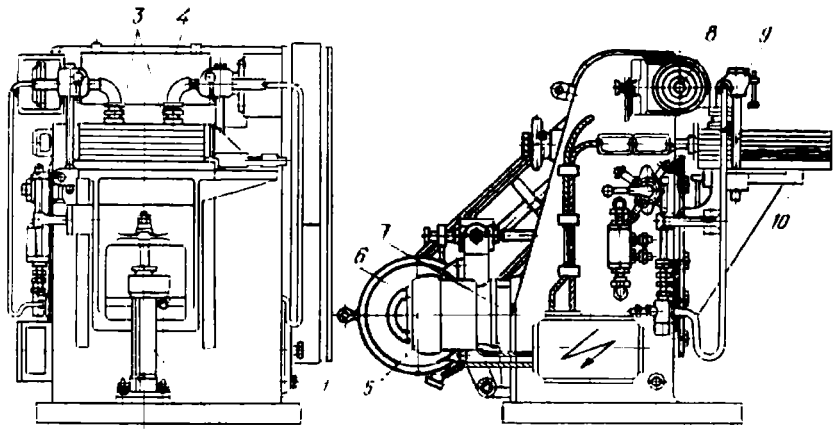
Общий вид одностороннего шипорезного станка ШПК40:
